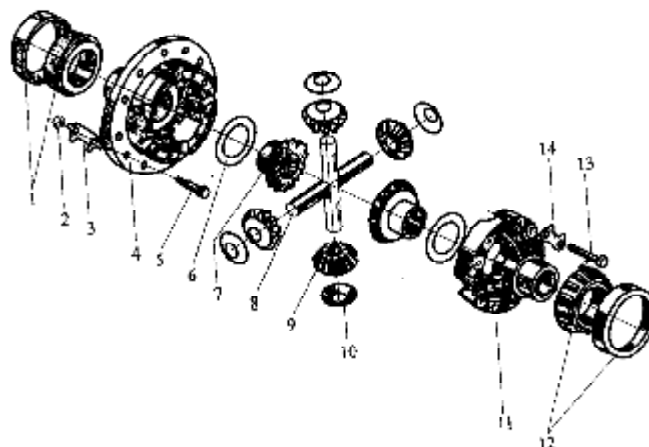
对称式圆锥行星齿轮差速器结构示意图
